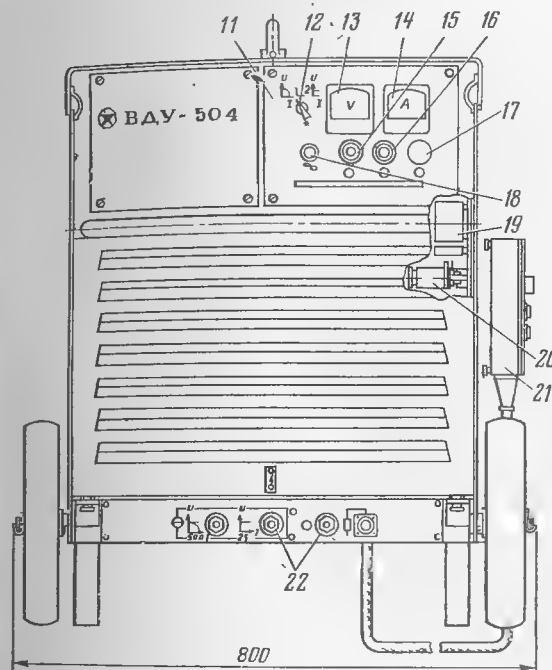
Сварочный выпрямитель ВДУ-504.
